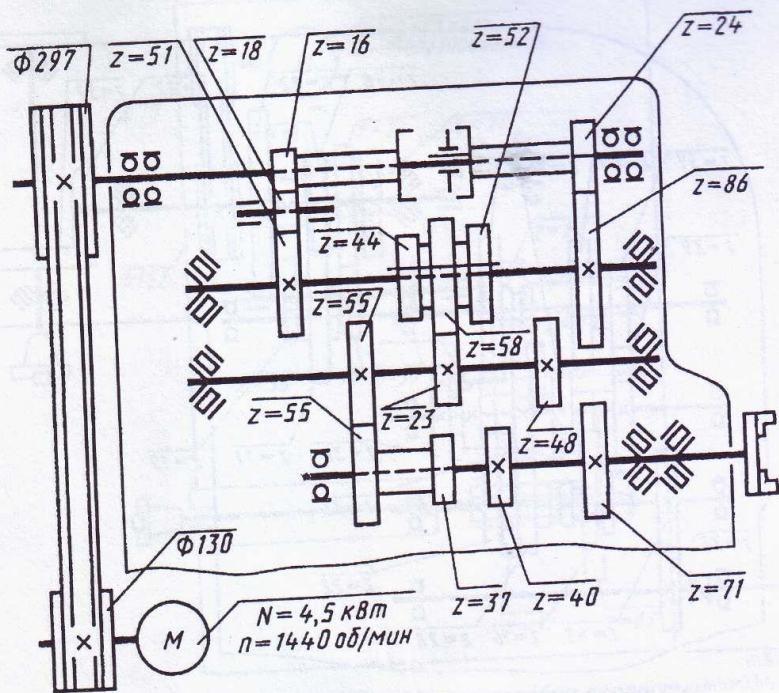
Кинематическая схема коробки скоростей токарно-револьверного станка 1П326
